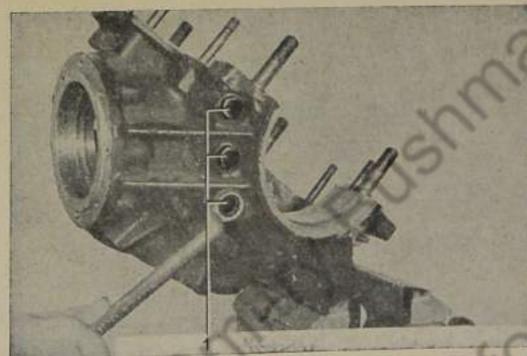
Lagerbock für Zylinderrollenlager abschrauben
